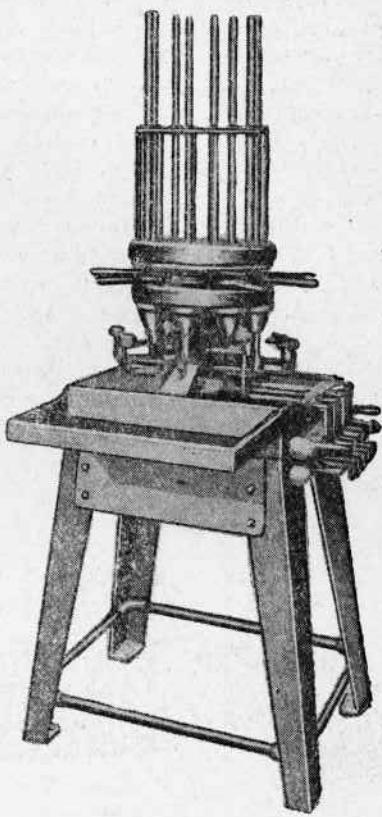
Комбинированный станок резки трубок и развертки тарелочек.
